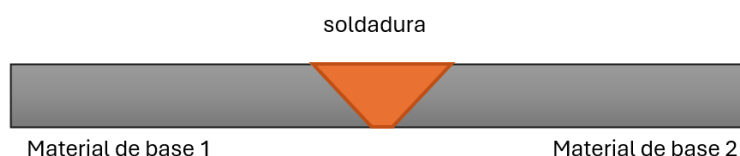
Exemplo de uma soldadura de topo
